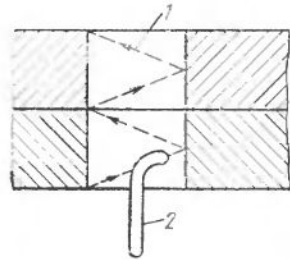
Траектория движения вихретокового датчика при контроле внутренней поверхности отверстия
